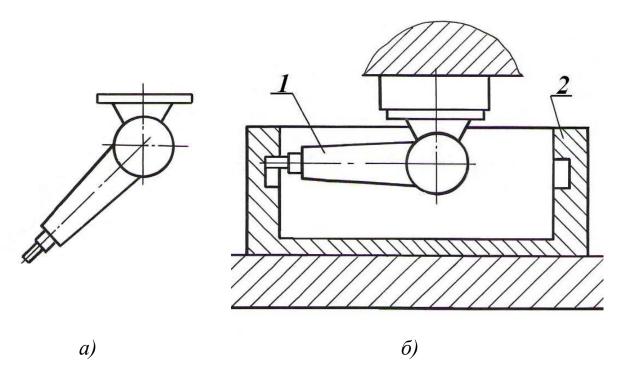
Съемная угловая шпиндельная головка: a — головка как конструктивный элемент; δ — головка в рабочем положении; l — шпиндельная часть головки; 2 — обрабатываемая деталь
